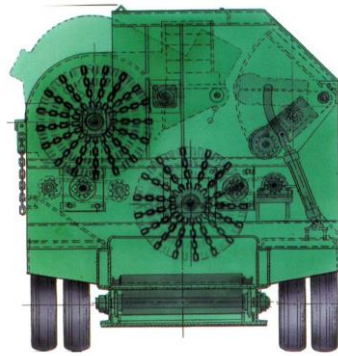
Поперечный разрез окорочного станка FD-2300 Husky Brute [109]
